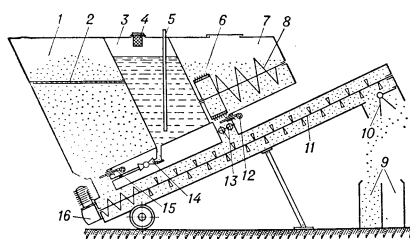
Смеситель отравленных приманок: 1 — зерновой бункер; 2 — сетка; 3 — резервуар для масла; 4 — заливная горловина с фильтром; 5 — уравнивающая трубка; 6 — щётки для очистки выходного отверстия бункера пестицидов; 7 — бункер пестицидов; 8 — проволочный шнек; 9 — тару; 10 — перекидная заслонка выгрузного отверстия смесителя; 11 — шнек-смеситель; 12 — заслонка выходного отверстия бункера пестицидов; 13 — дозирующие барабаны; 14 — регулировочный кран; 15 — заслонка зернового бункера; 16 — электродвигатель.
